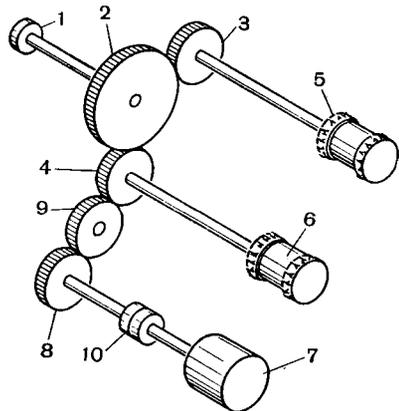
Кинематическая схема механизма, расположенного в кассете
